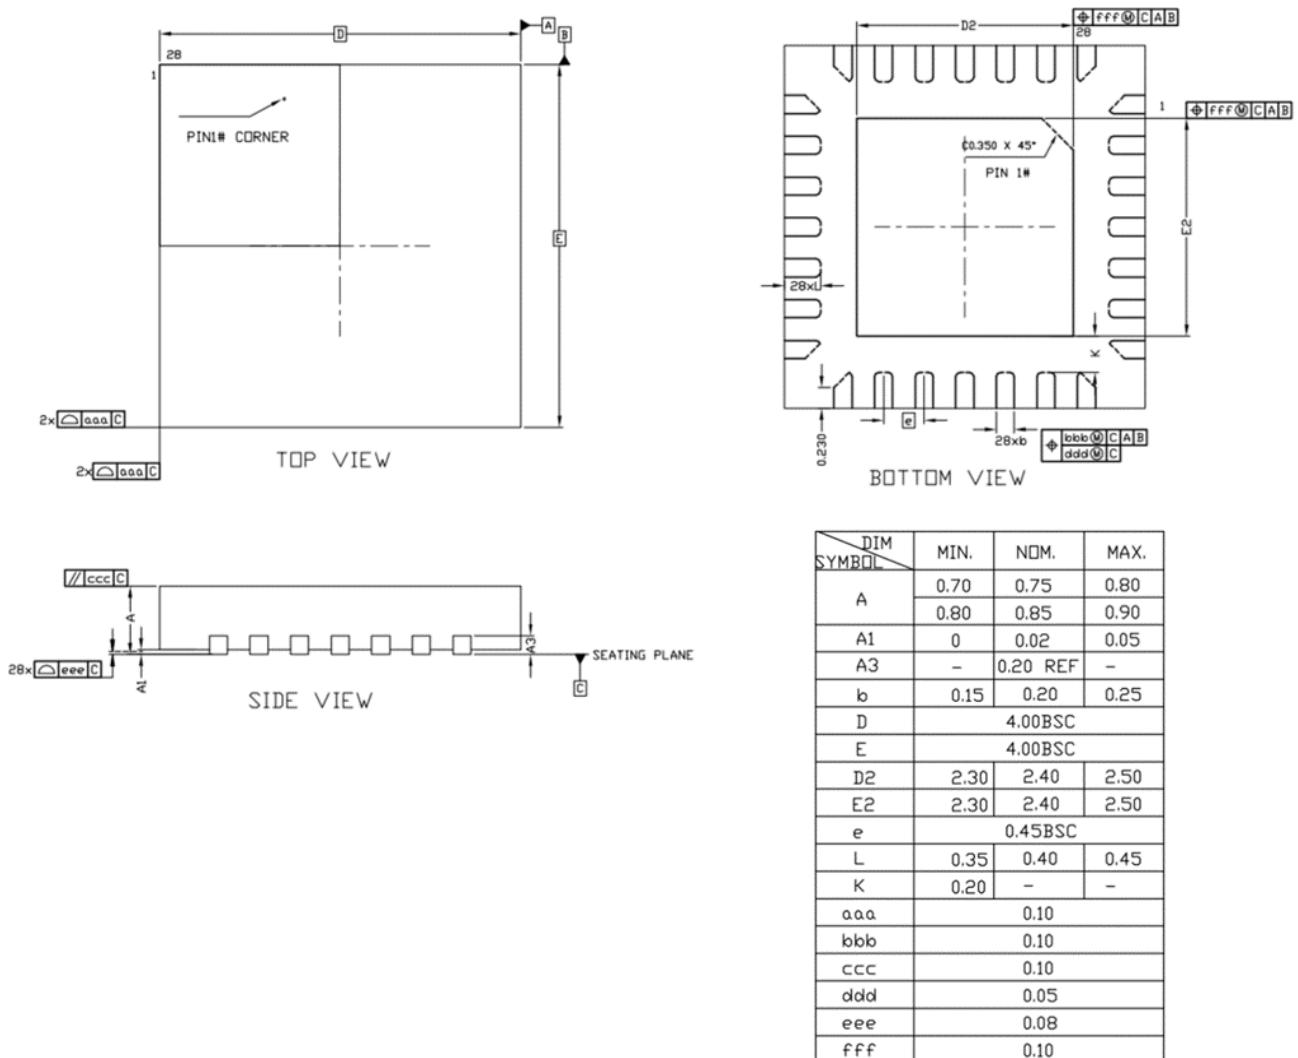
QFN28 (4*4*0.75-P0.45) 封装外形尺寸
